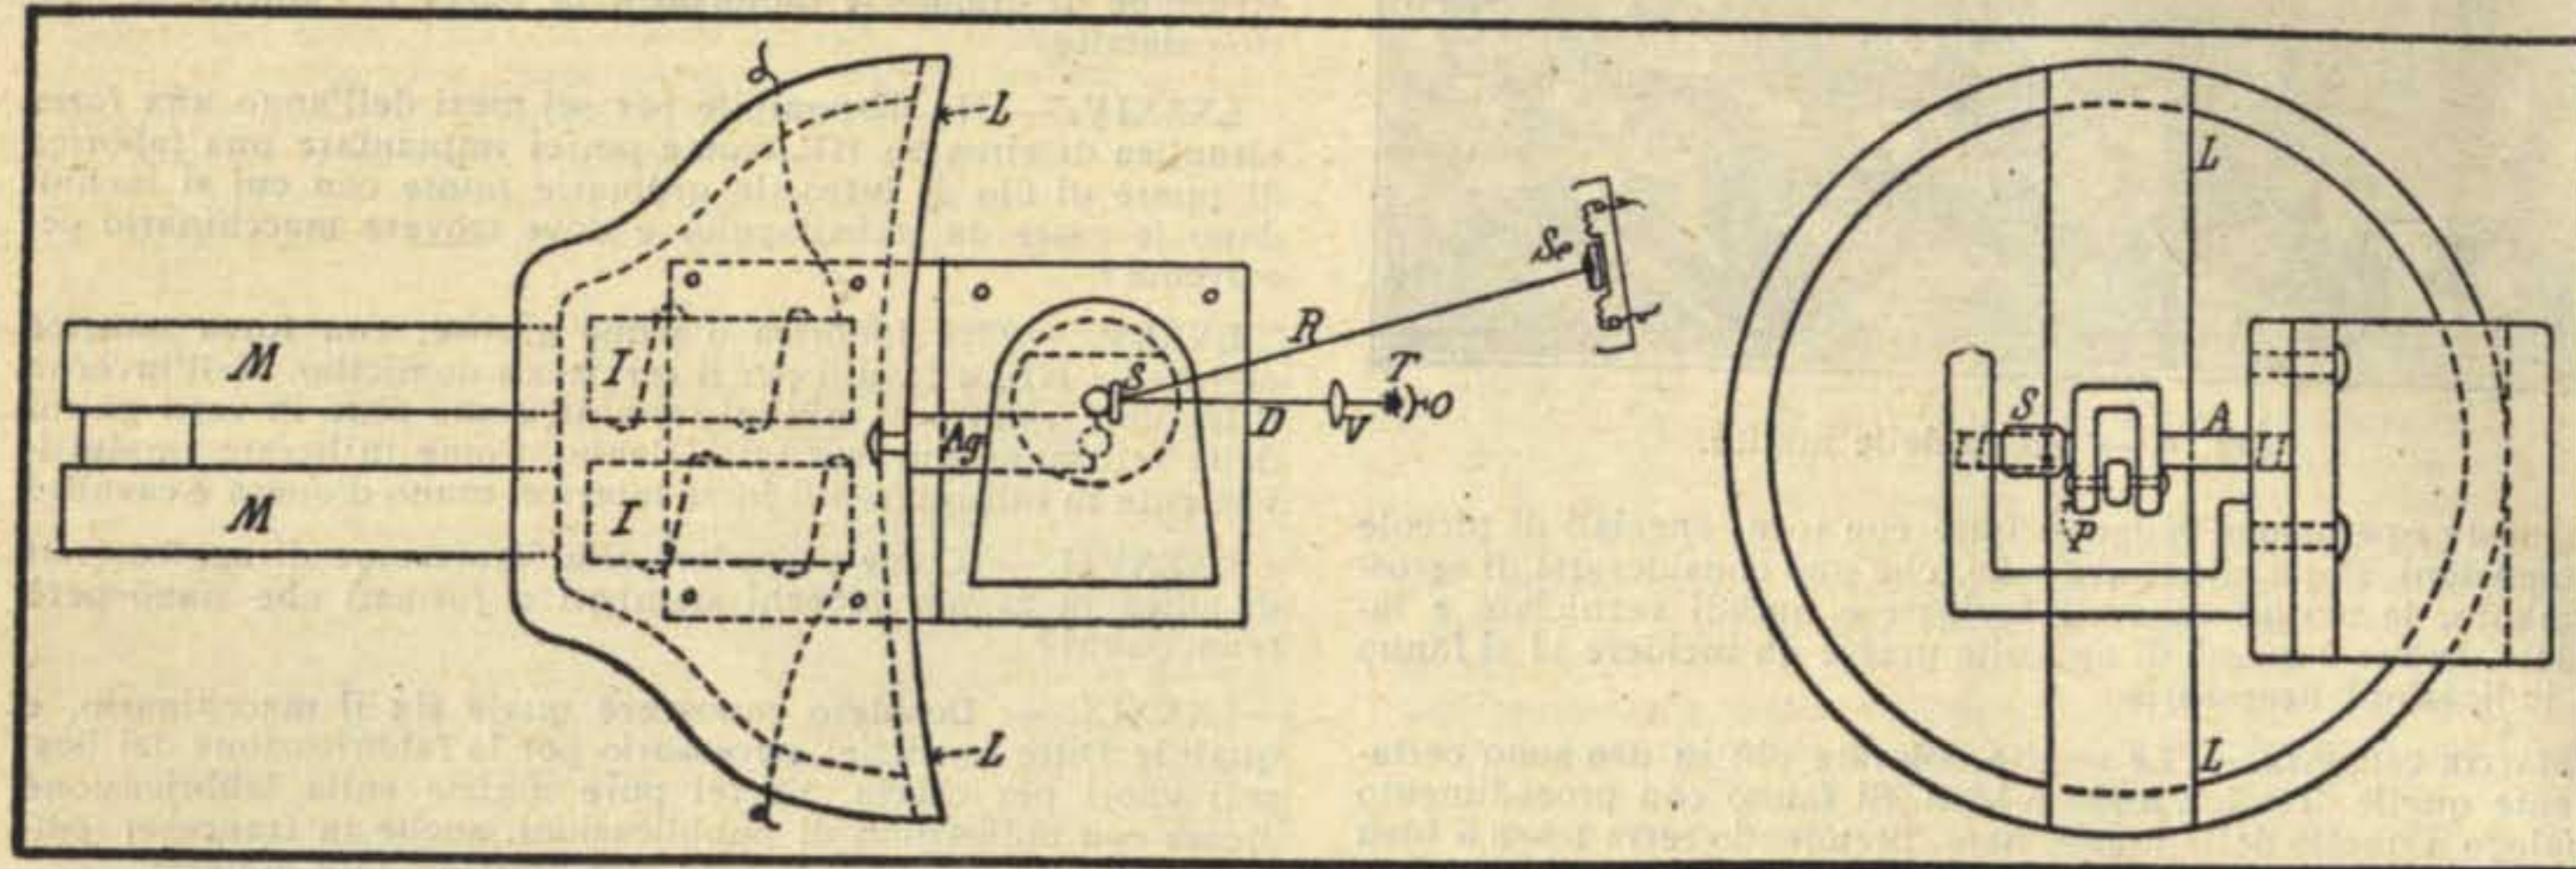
Dettaglio del meccanismo per la vibrazione degli specchi durante la scrittura: M, L, S, R, D, V, Se, O, T, come nella fig. 3. I, circuito induttore; Ag, asta di contatto in argento; A, albero montato su agata; P, spina distante un decimo di millimetro dall'asse centrale dell'albero.
